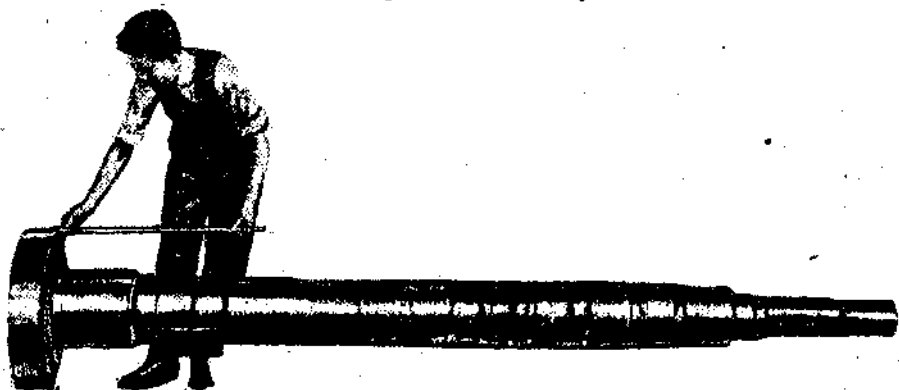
Вал с неправильно выточенными заплечиками подготавливается для автоматической дуговой сварки.
